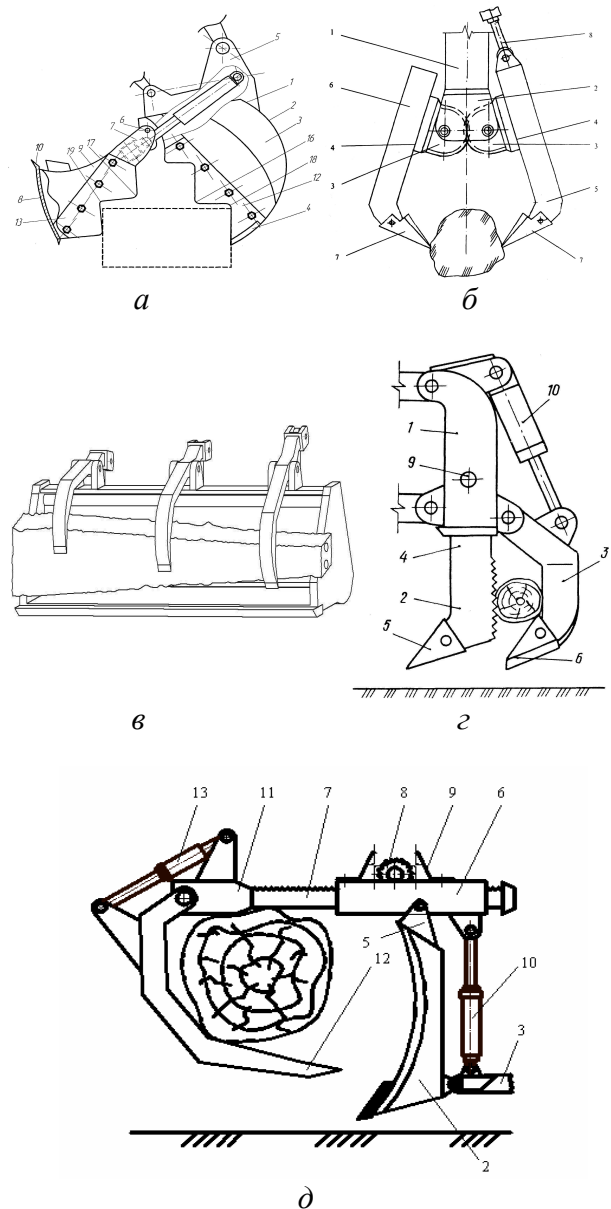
Засоби механізації, які розроблені для розбирання завалів: а - щелепний ківш екскаватора; б - захват екскаватора; в - ківш із захватами навантажувача; г - розпушувач із гідрокерованими зубцями; д - бульдозер із захватами
